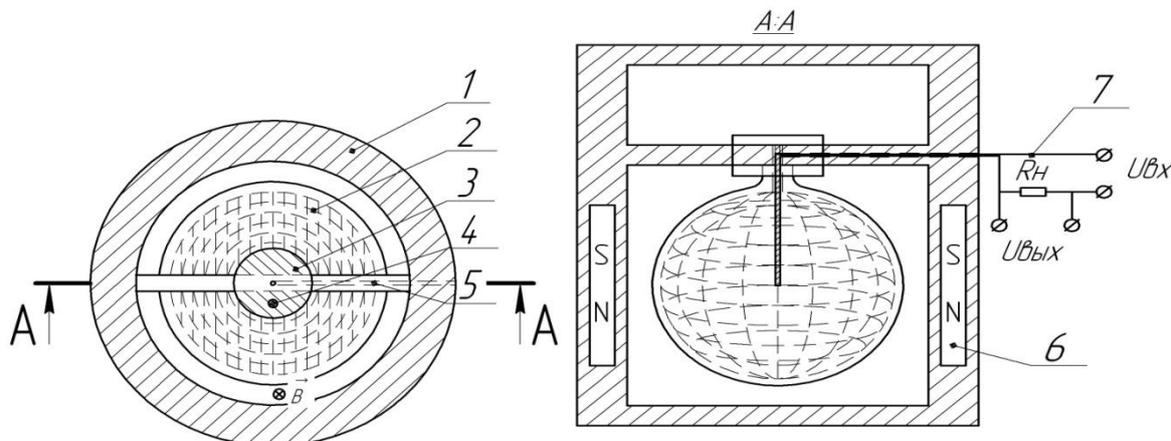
Композитный чувствительный элемент ШЭМД: 1- диэлектрический композитный корпус; 2- эластичный композитный чувствительный элемент с металлокордом; 3 – неподвижный элемент; 4 – крышка отводящего воздушного канала; 5- неподвижная ось; 6 – постоянные магниты, расположенные друг относительно друга противоположными полюсами и закреплённые на внешней стенке корпуса; 7 – электрические выводные концы, одним концом закреплённые на вертикальной штанге, другим – в верхней точке.
